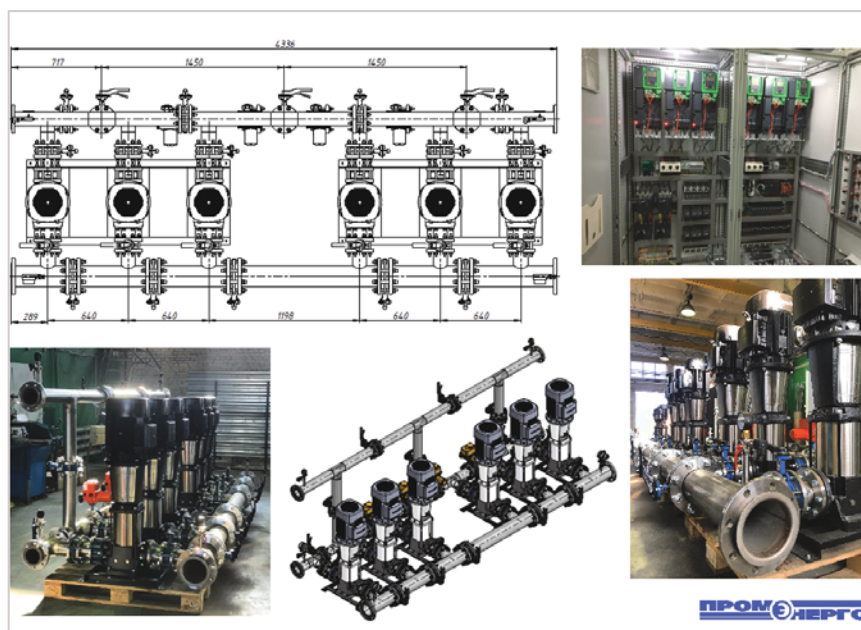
Габаритный чертеж и внешний вид МАНС МультиПро 6 CR 64-3-1 Ч+опц
